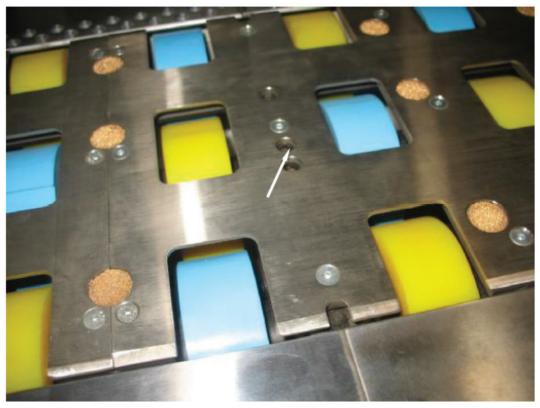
Llenado de leva del alimentador. Boquilla de crema de rodillos del alimentador (simétrico). Tipo de llenado: Tipo A
